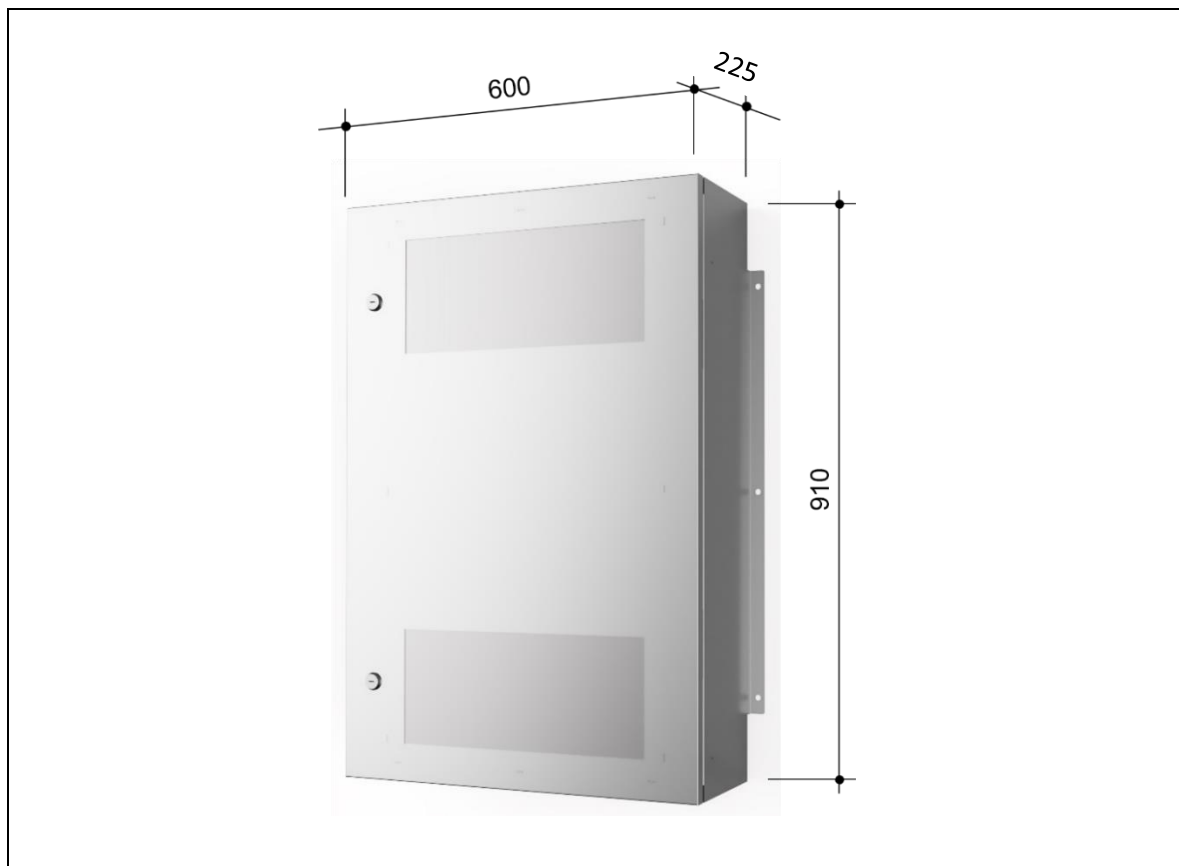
Gehäuse Wechselrichter – Abmessungen
